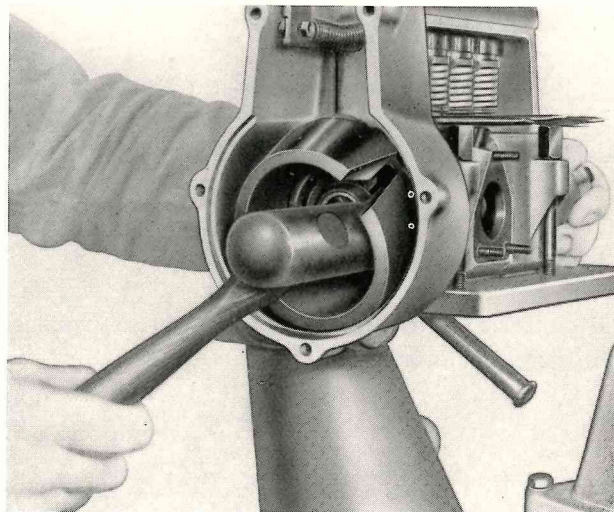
Smontaggio dell'albero ad eccentrici.
